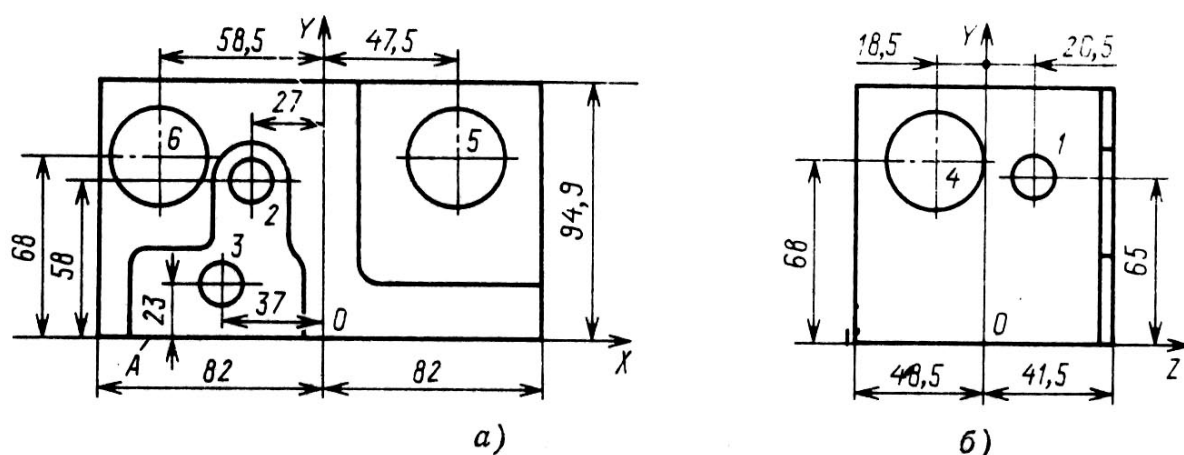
План обработки заготовки; *a* – со стороны II; *б* – со стороны I
